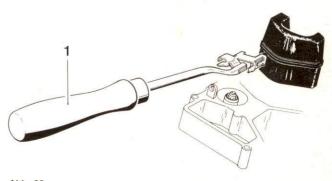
1) Weber-Werkzeug Best, Nr. 98.0239.50
